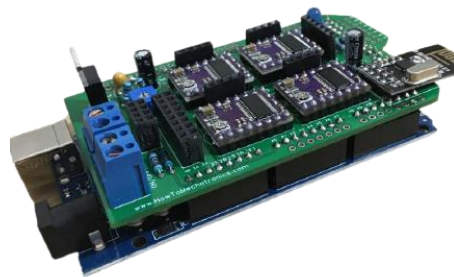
PCI com os componentes soldados ligada ao arduíno.
